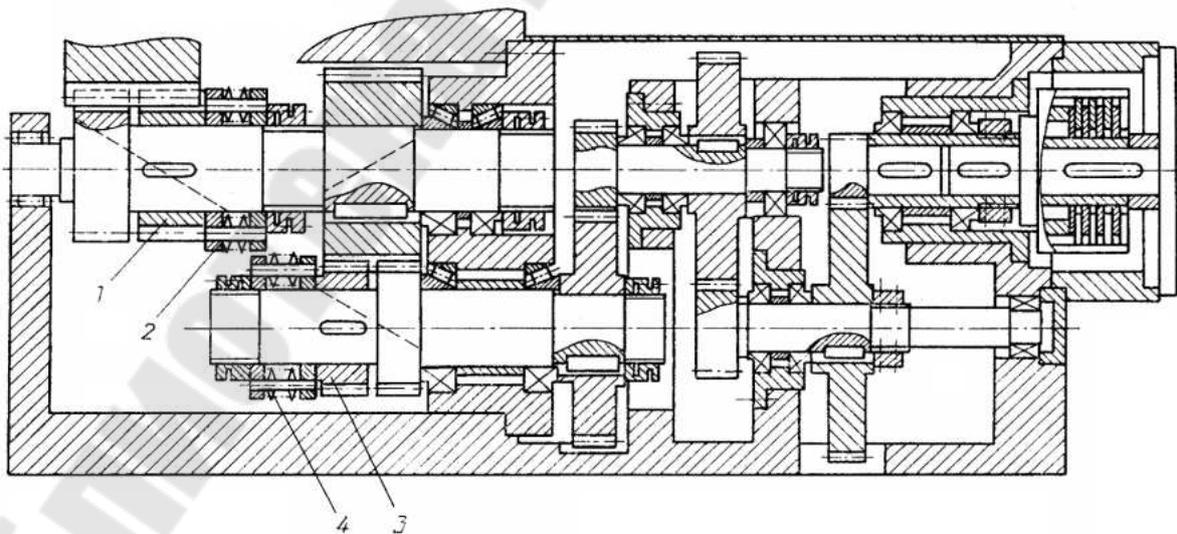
Привод колесо–рейка с выборкой зазора
